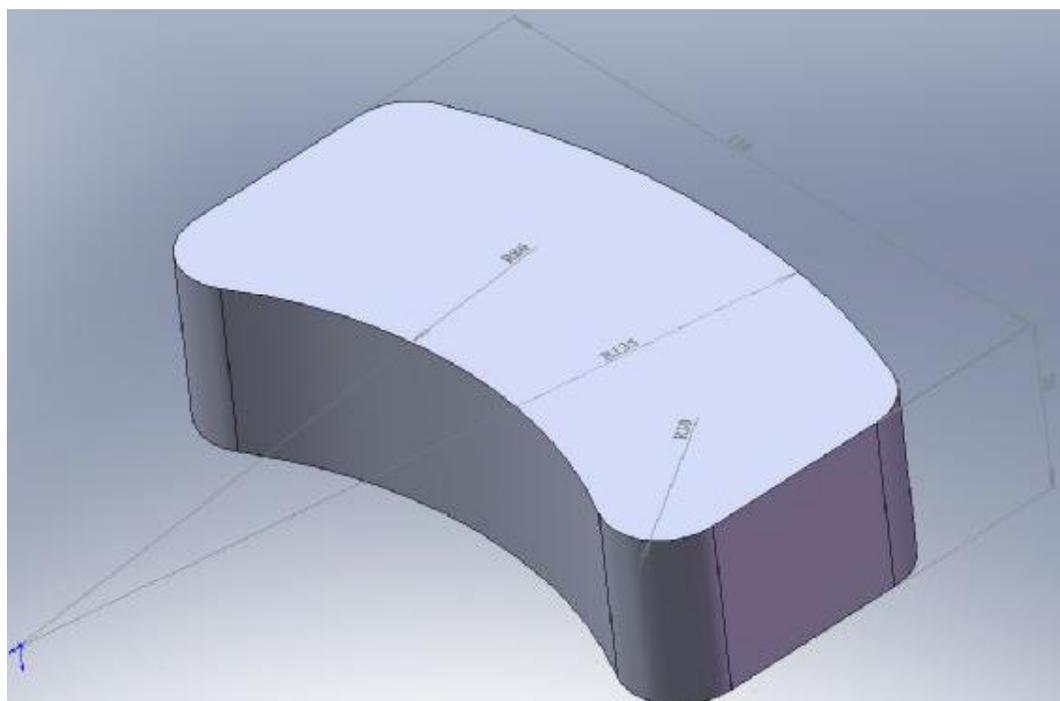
Шейка легкоудаляемой прибыли для отливки
